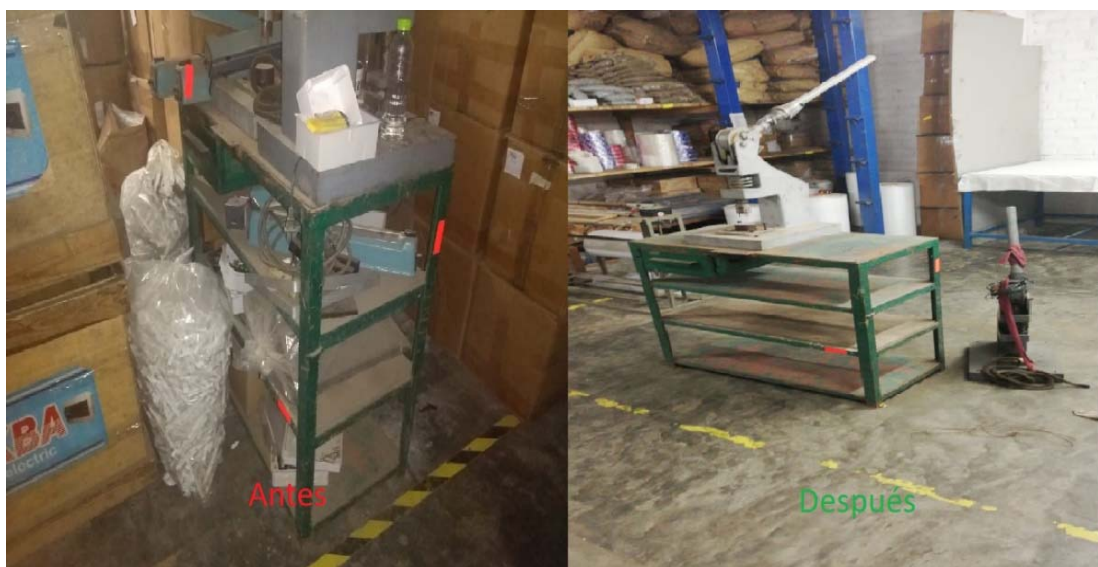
Aplicación de la primera S en el área de Empaquetado
